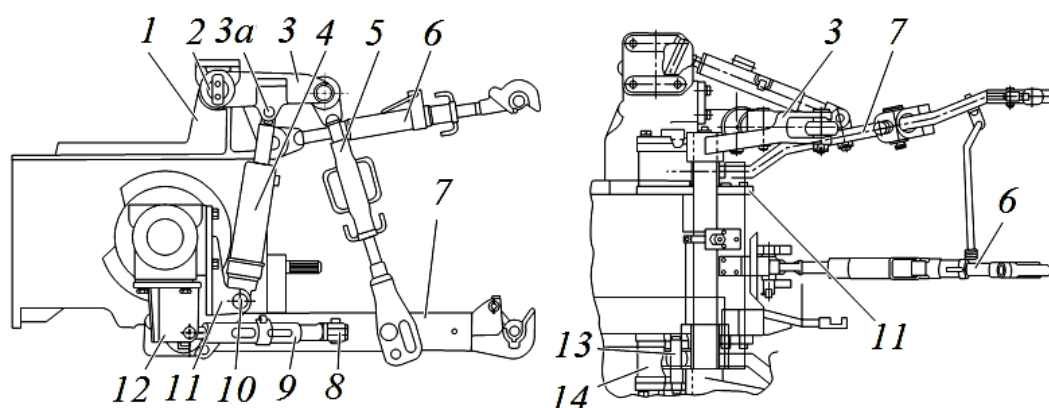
Заднее ПНУ трактора «Беларус-1523»: 1 – крышка заднего моста; 2 – поворотный вал; 3 – наружные рычаги (левый и правый); 3а – пальцы штоков гидроцилиндров; 4 – гидроцилиндры; 5 – раскосы; 6 – верхняя тяга; 7 – нижние тяги; 8 – проушины; 9 – стяжки; 10 – пальцы; 11 – кронштейны; 12 – кронштейны стяжек; 13 – пальцы (силовые датчики); 14 – кронштейны
